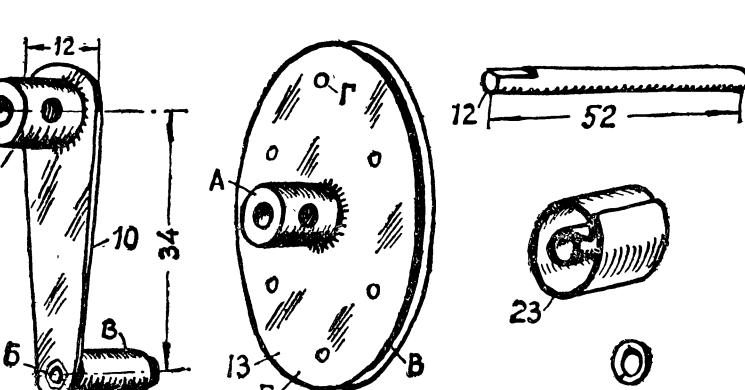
Детали привода: 10 — рукоятка; 12 — ось; 13 — ведущий шкив; 23 — приемная бобина
